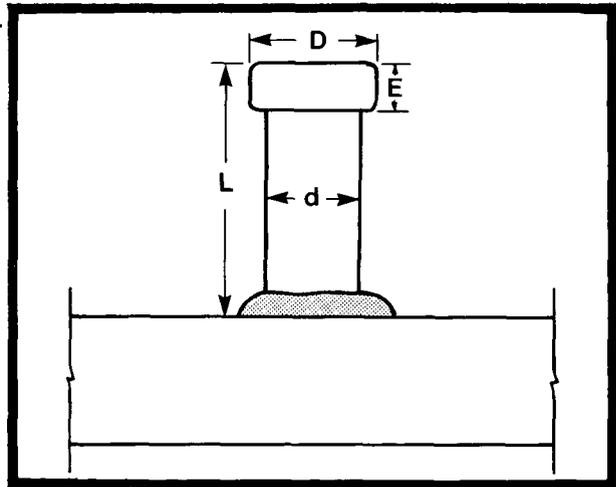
SOUDAGE DES GOUJONS
